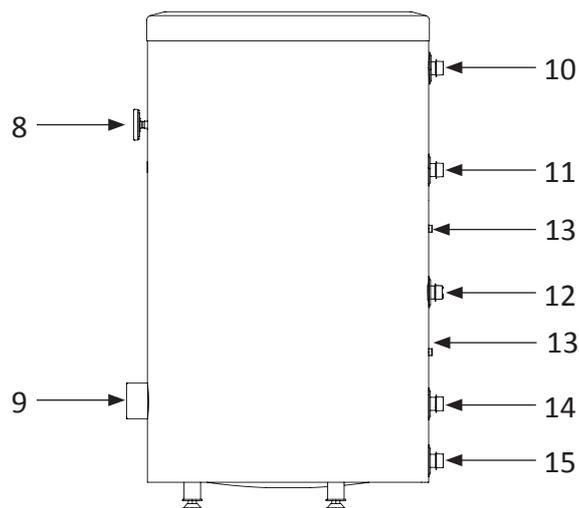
Вид сбоку водонагревателя W-E 100-125.81R.
